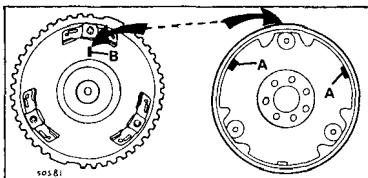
Сварные швы ведущего диска (А) должны быть обращены к гидротрансформатору (В)
